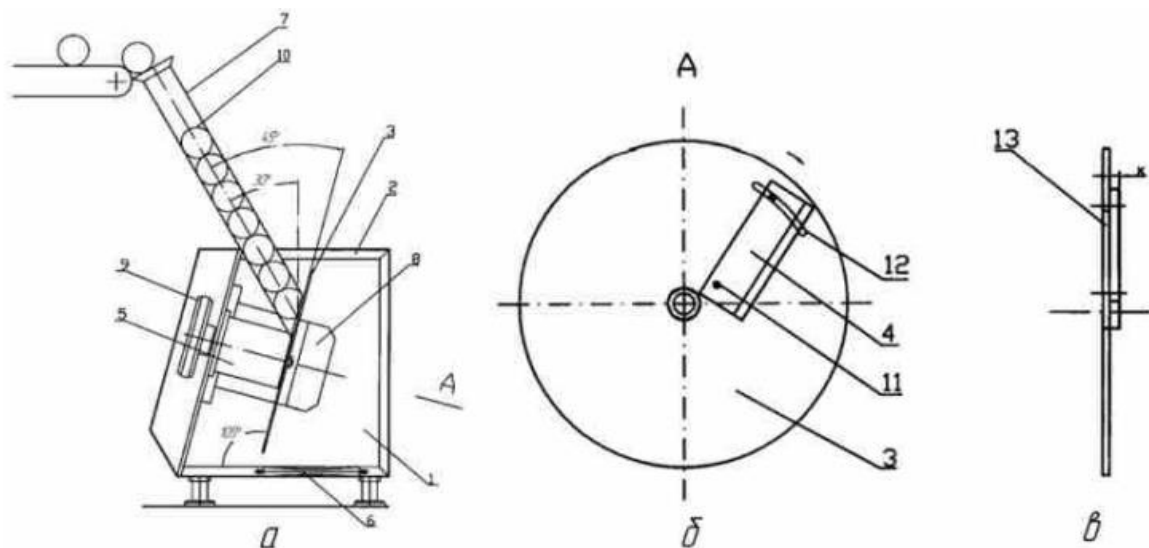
Пристрій для різання овочів та фруктів
